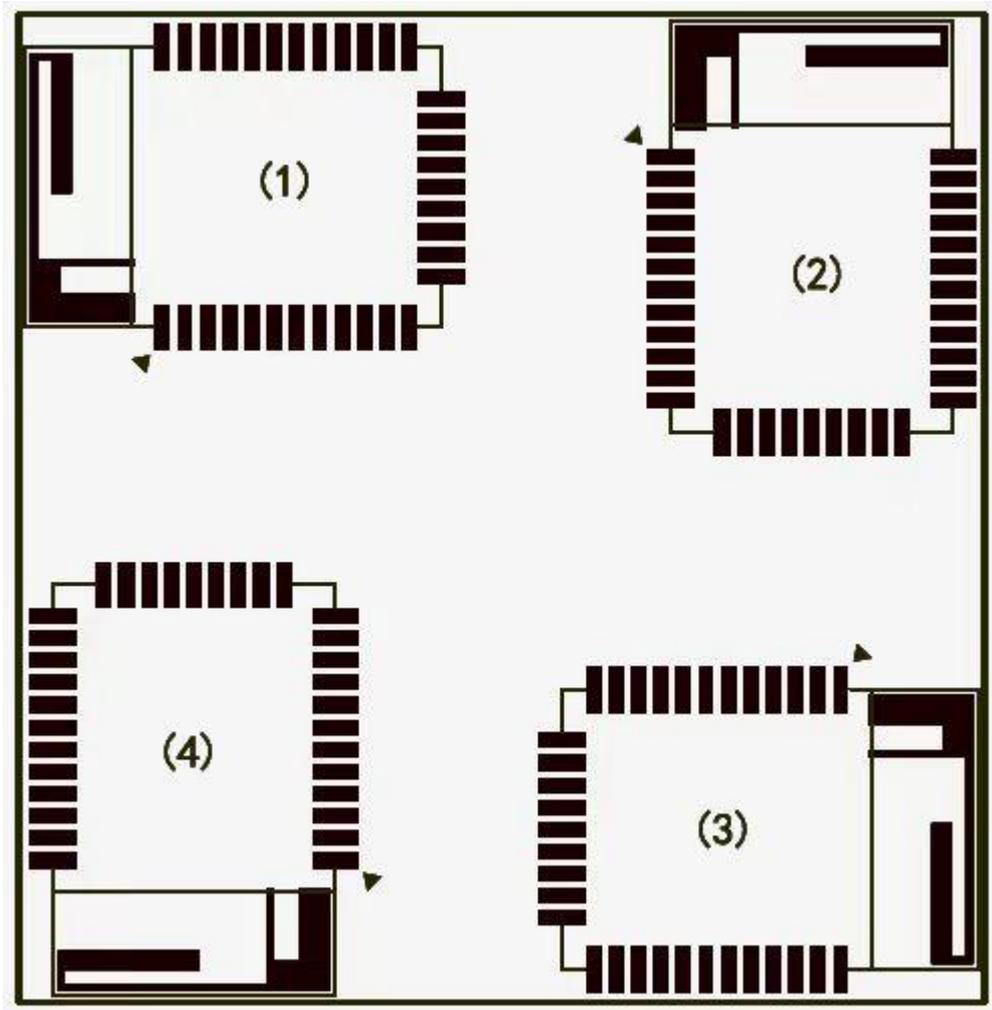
LZM1-FR16 模块在 PCB 上的 4 种摆放方式
